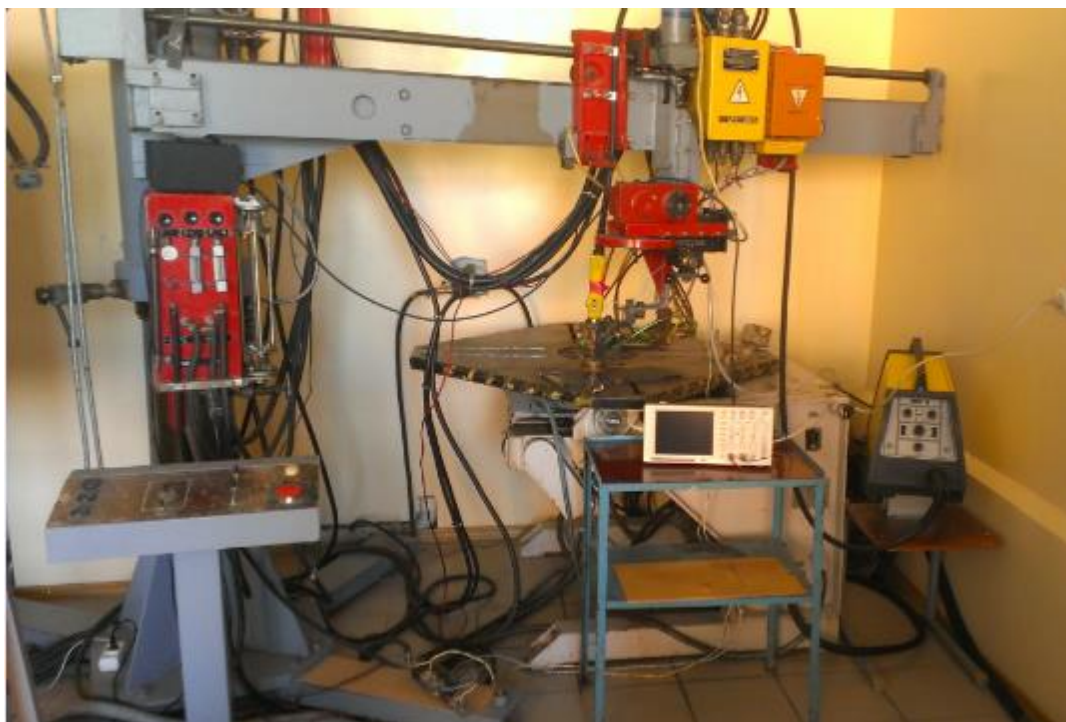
Общий вид установки УПН–303 для плазменной сварки-наплавки плавящимся электродом
